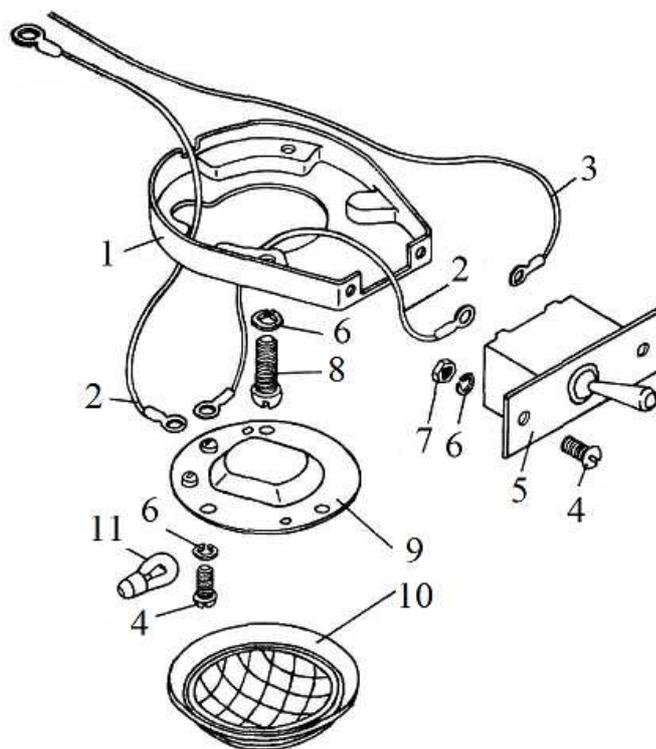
Плафон освещения кабины, габаритные размеры
